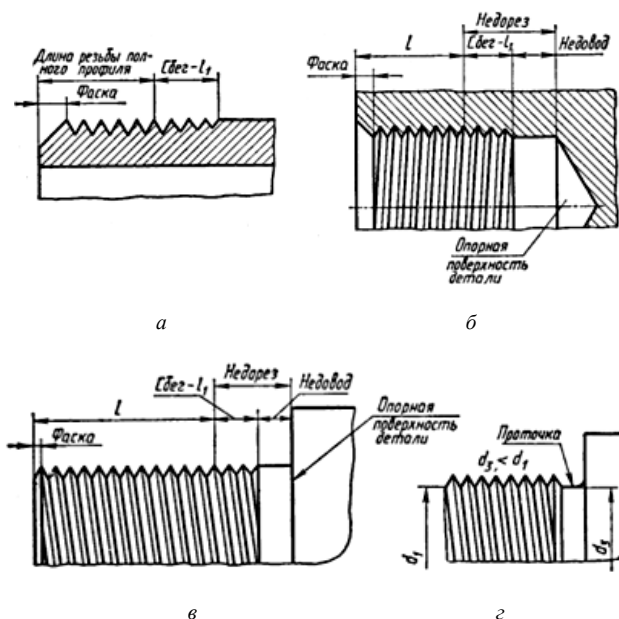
Элементы резьбы: а – фаска и сбеги; б, в – фаска, сбеги, недорез, недорез; г – проточка
